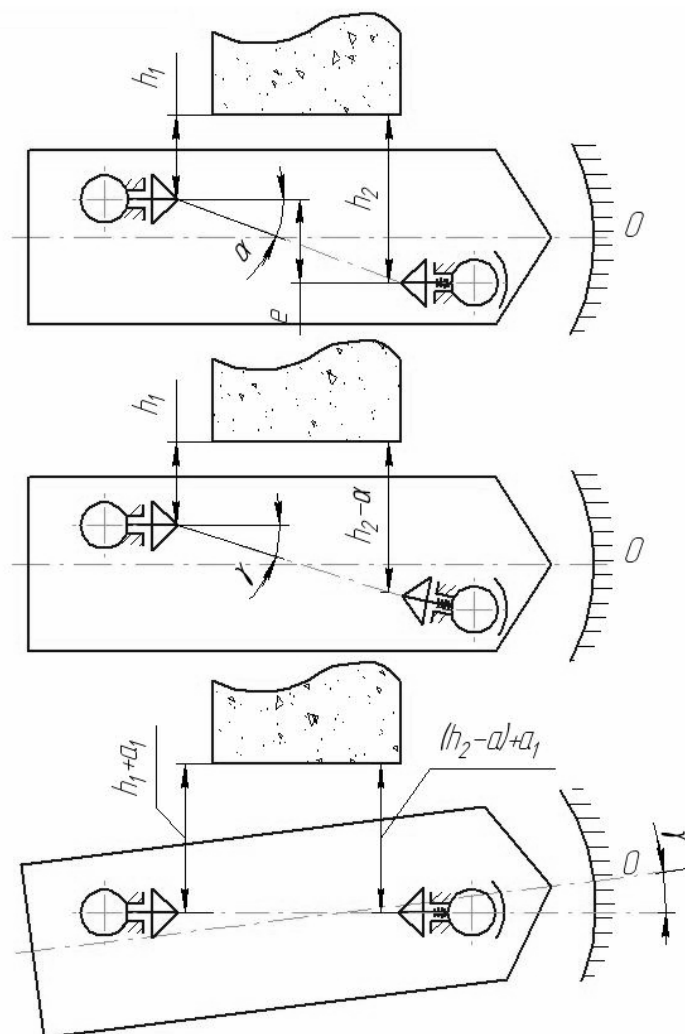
Схема регулировки положения задней бабки и стола станка
